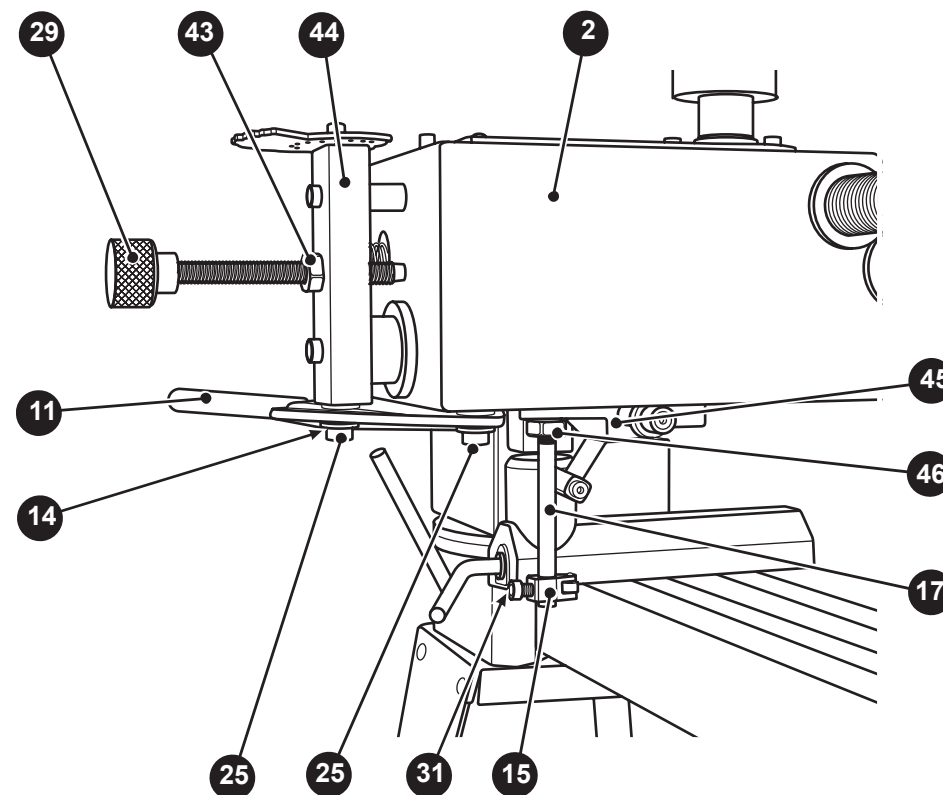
Рисунок N — монтаж держателя на стойку (с правой стороны станка) для последующей установки плоского шаблона.
